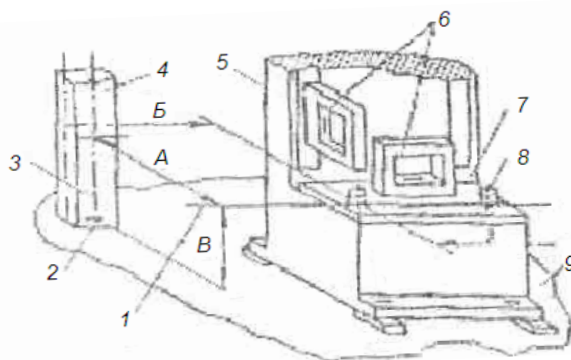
Лазерный комплекс уровня: 1 – лазерный луч; 2, 3 – базовые отметки (плашка, репер); 4 – колонна; 5 – станок; 6 – уровни; 7 – базовая поверхность для установки заготовки; 8 – фиксатор; 9 – чистый пол
